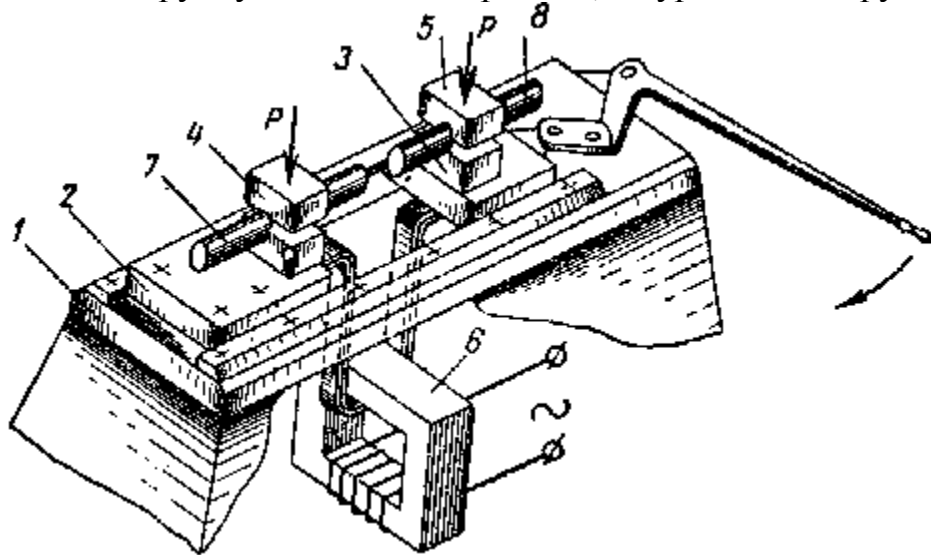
Схема машины для стыковой контактной сварки
